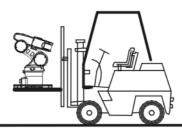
Transporte con carretilla elevadora de horquilla
